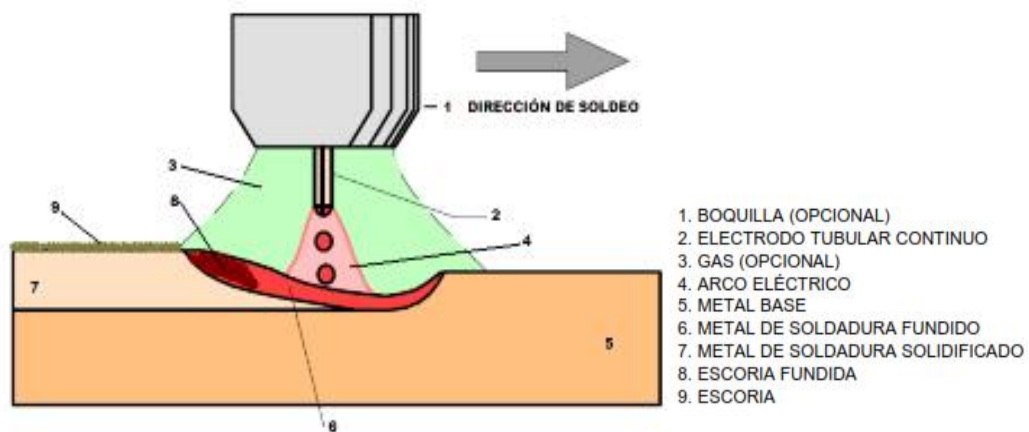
Soldadura con alambre tubular con protección gaseosa
